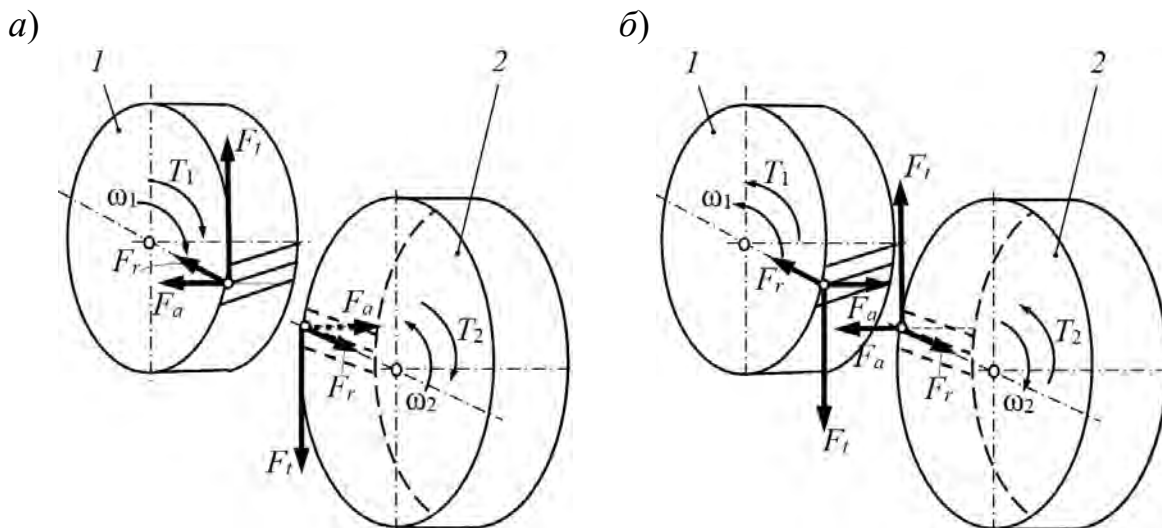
Силы в косозубом зубчатом зацеплении при вращении шестерни по часовой стрелке (а) и против часовой стрелки (б): 1 – шестерня; 2 – колесо
